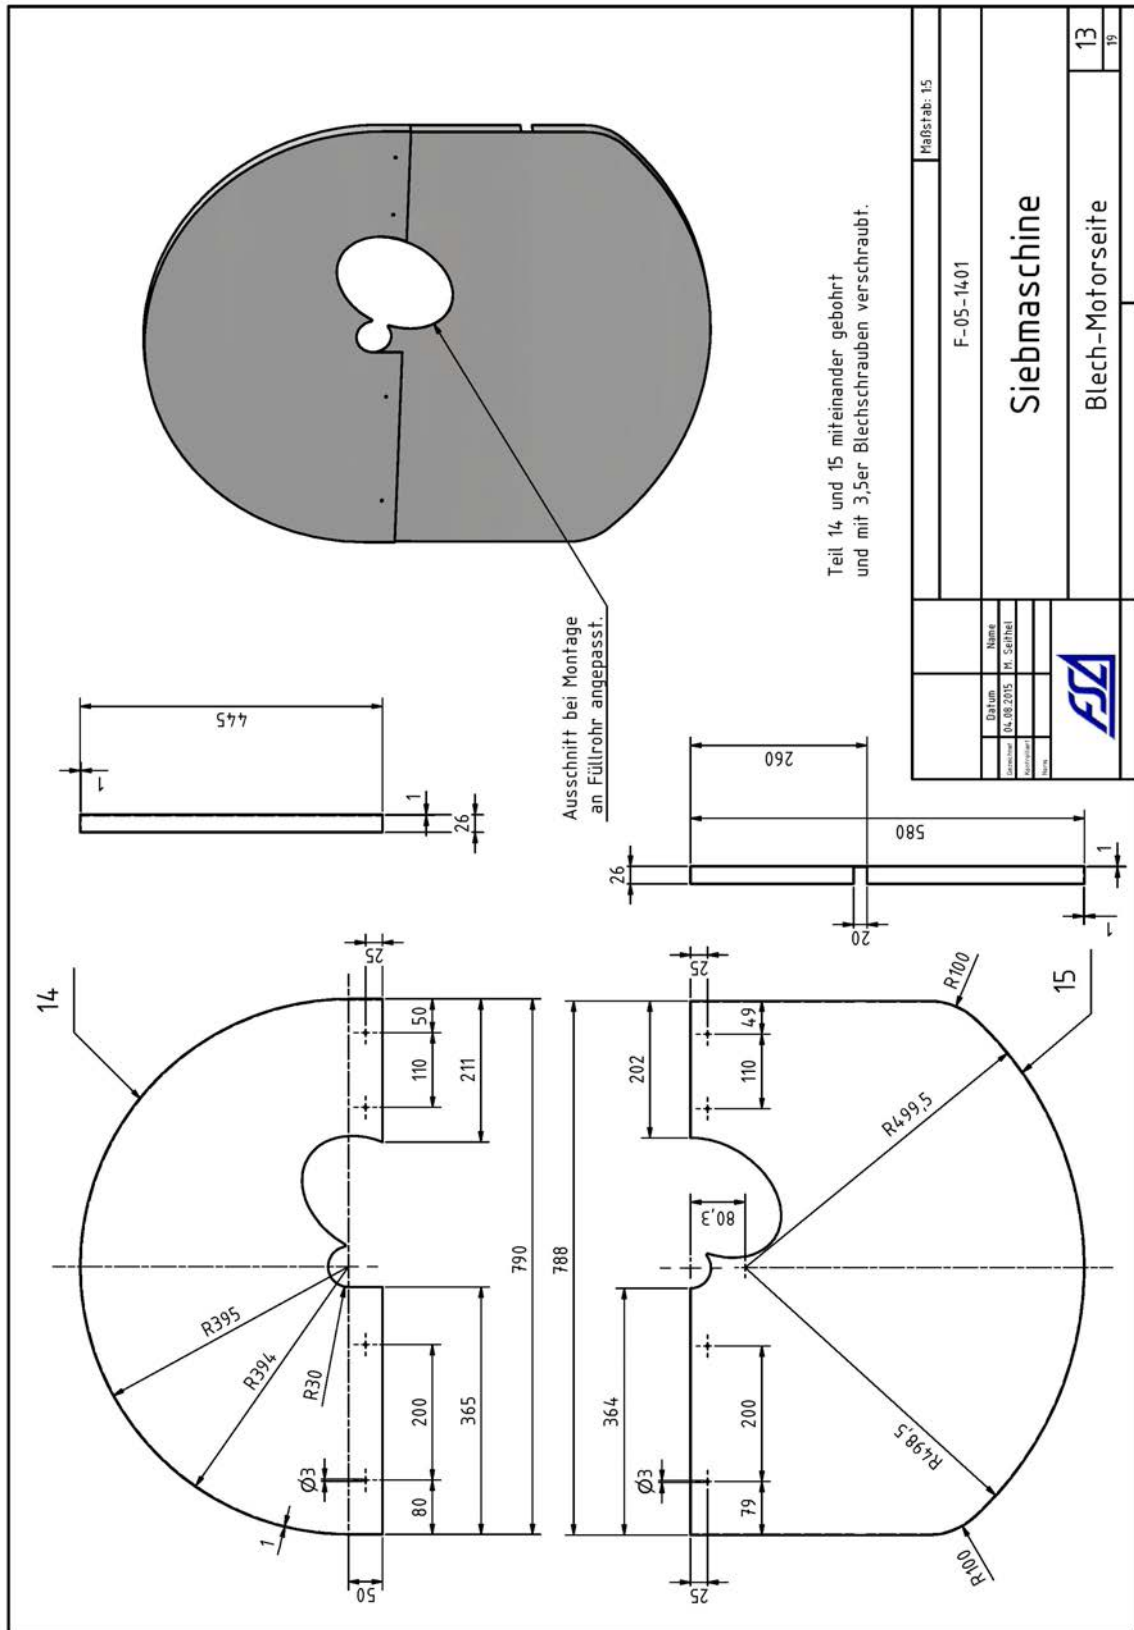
Konstruktionszeichnung zur Siebmaschine.
